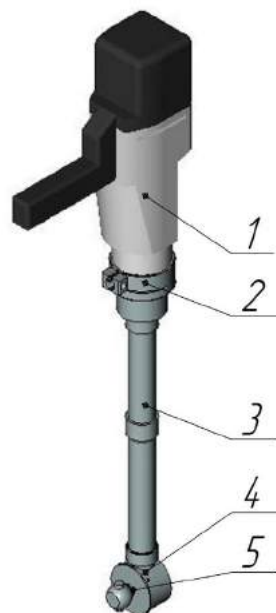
Предлагаемая конструкция станка: 1 – привод; 2 – верхний редуктор; 3 – консоль привода; 4 – нижний редуктор; 5 – выходной вал со встроенной шарнирной муфтой
